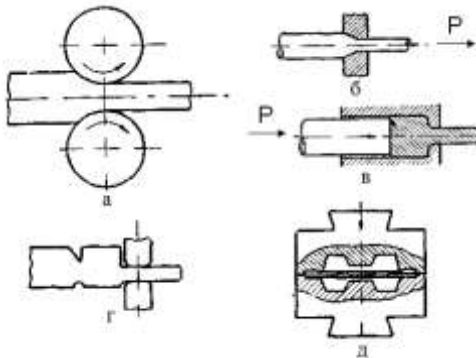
Схеми обробки заготовок тиском: а – прокатування; б – волочіння; в – пресування; г – кування; д – штампування металу, що призводить до його розтікання в порожнині інструмента.
